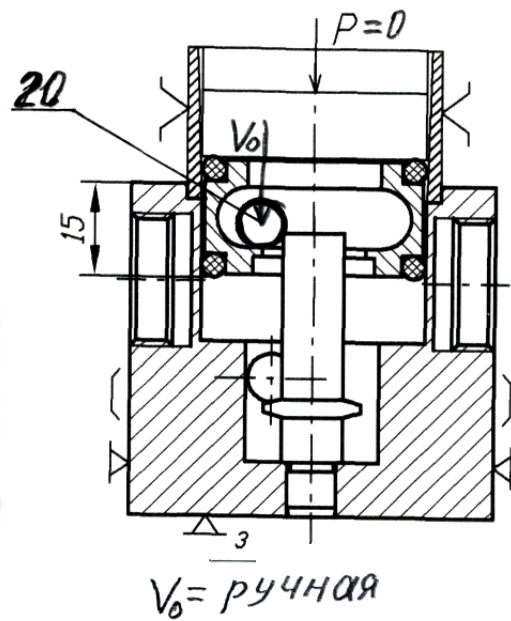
Эскиз установки втулки 3 с кольцами 14 в корпус.
